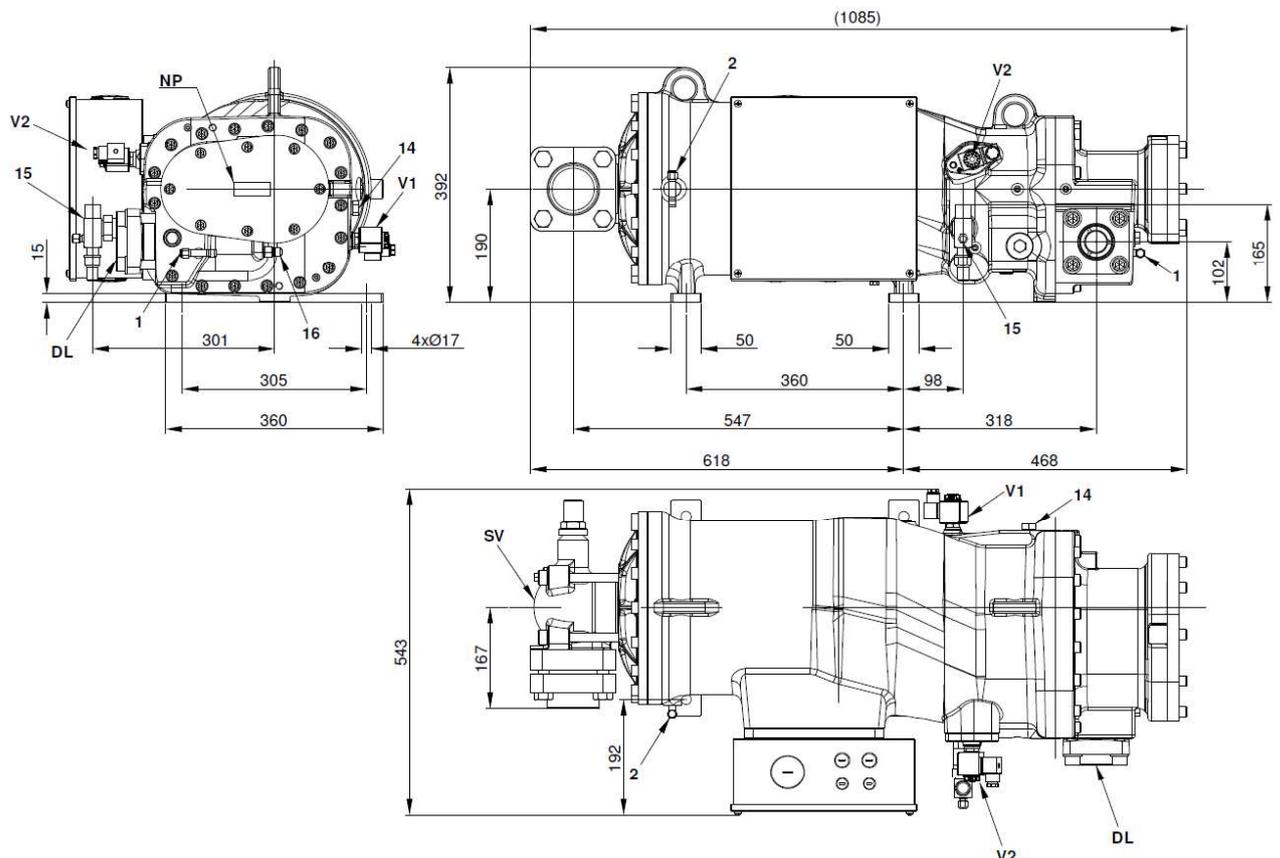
Габаритные размеры винтового компрессора FVR-L-60-200
